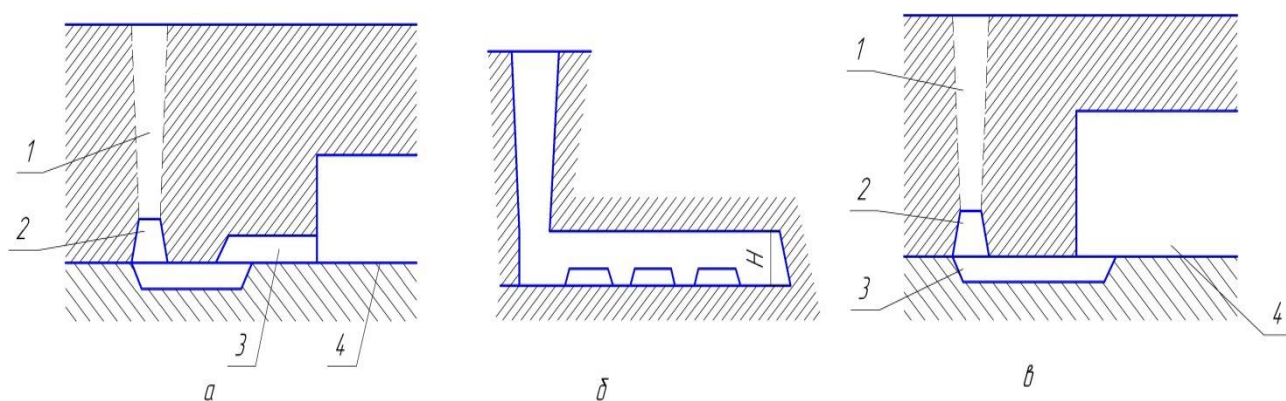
Подвод металла в форму: *а* - ступенчатый питатель; *1* - стояк; *2* - шлакоуловитель; *3* - ступенчатый питатель; *4* - отливка; *б* - плоский питатель в верхней опоке; *в* - нерекомендуемый способ подвода питателя снизу под отливку
